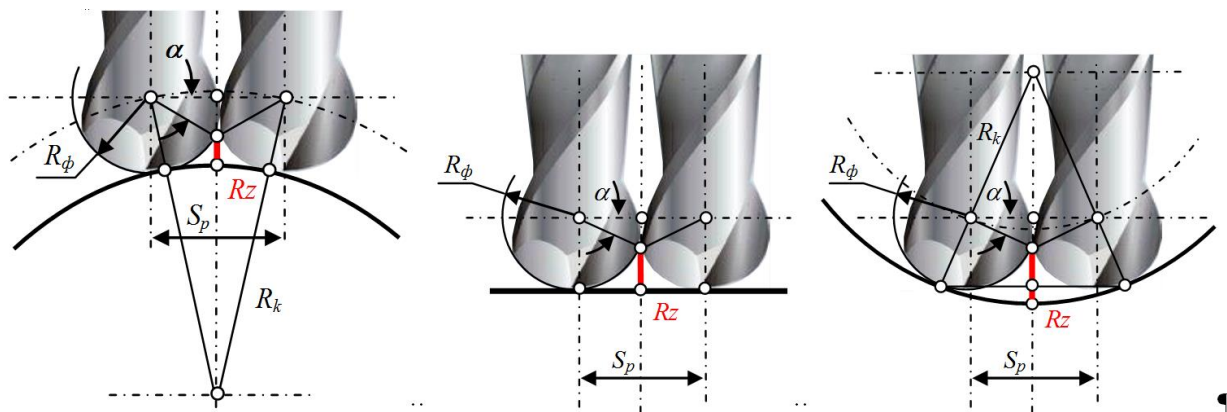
Схеми формоутворення для поверхонь:
